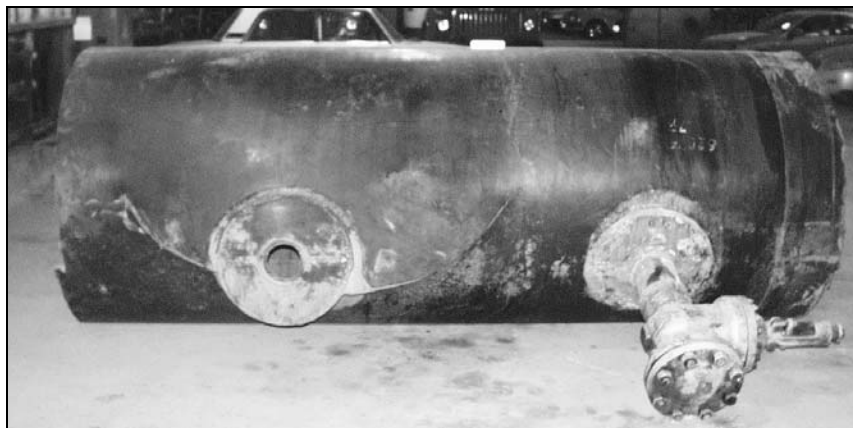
Внешний вид разрушенного участка трубы (аварийной катушки)
